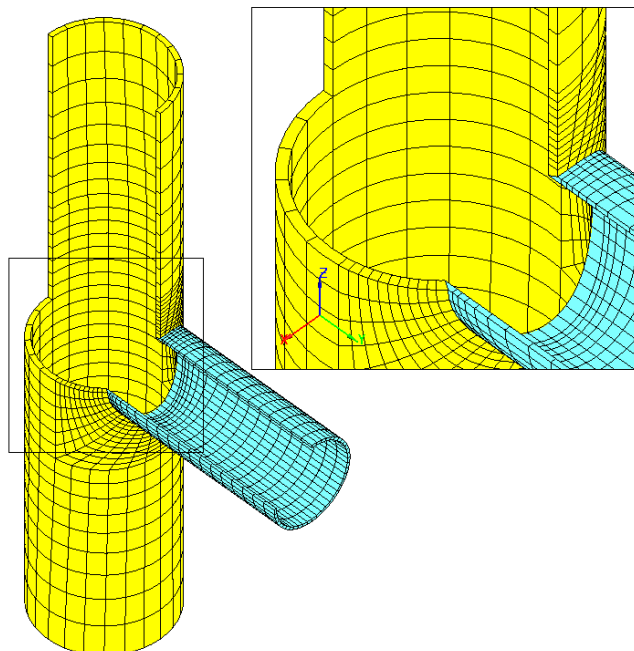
Тройник сварной с зачищенным швом. ИПКЭ16 (ИПКЭ20) многослойная схема
